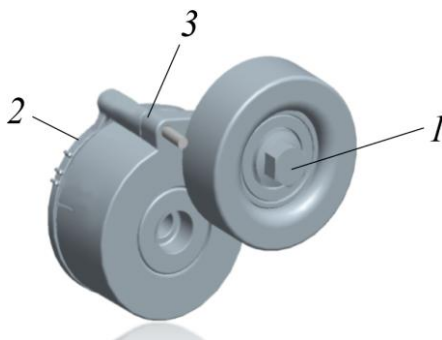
Натяжное устройство ремней двигателя ЯМЗ-534
